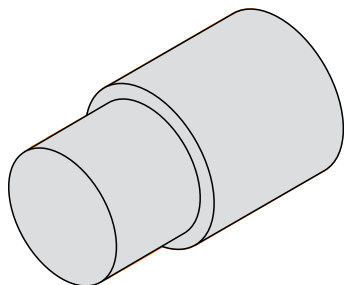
Образцовая деталь – Черновая обработка внешнего контура
